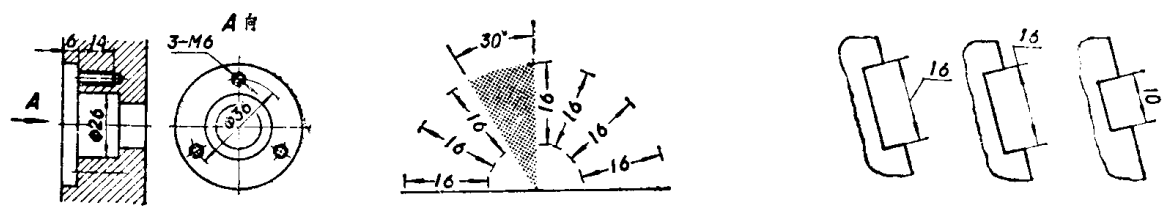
尺寸数字标注 图 1-9 尺寸数字方向 图 1-10 在 30° 范围标尺寸方法
